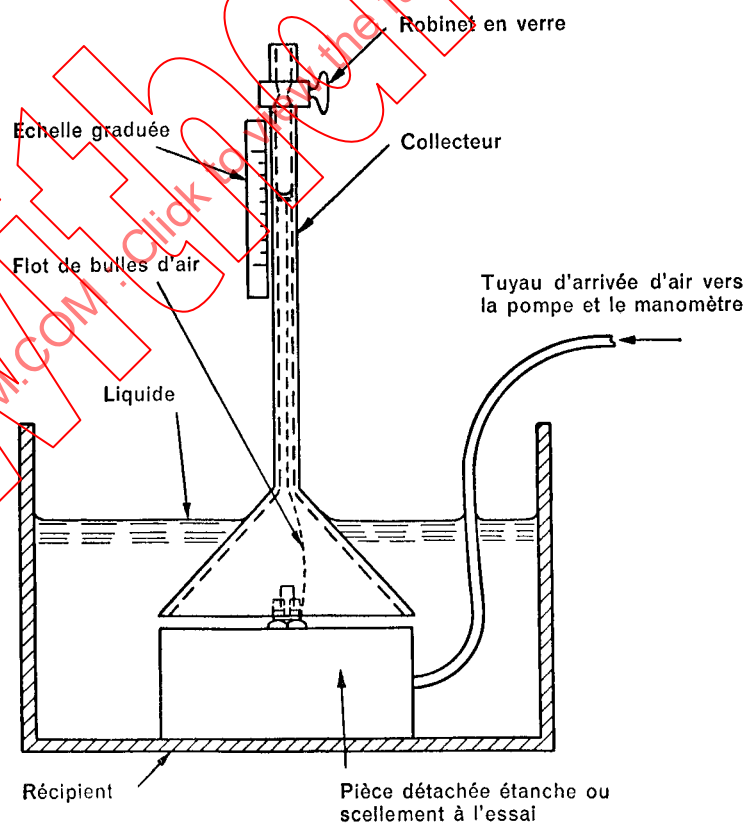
(Essai Q) — Schéma du dispositif pour l'essai d'étanchéité des passages
